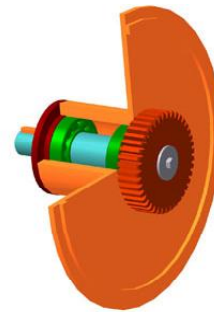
Модель збірки деталей сонячного зубчастого колеса
